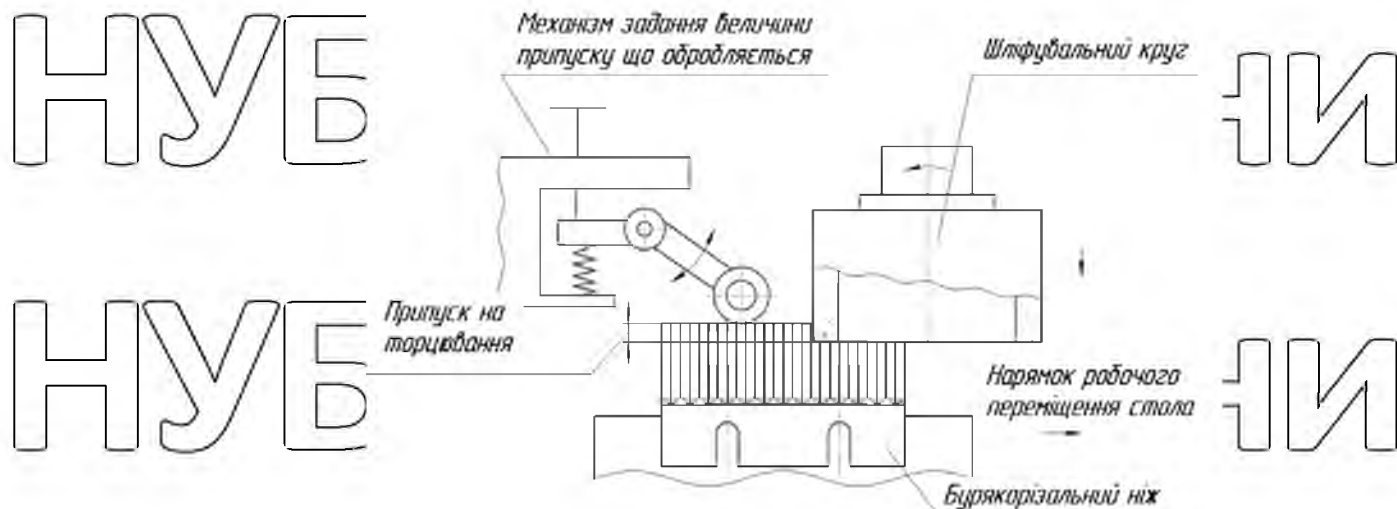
Схема установки для торцювання ріжучих крайок
